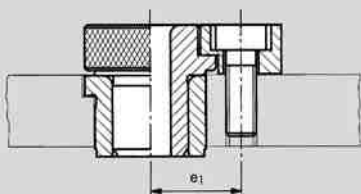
Schnellwechslbuchse Form K mit eingelassener Bundbohrbuchse DIN 172 oder zylindrischer Bohrbuchse DIN 179. Die Befestigung erfolgt mit Spannbuchse DIN 173 und Zylinderschraube DIN 912. Die Schnellwechslbuchse Form K kann auch mit Anschlagstift gesichert werden. Diese Befestigungsmöglichkeit ist nicht für langspanende Werkstoffe vorzusehen (Unfallgefahr).
